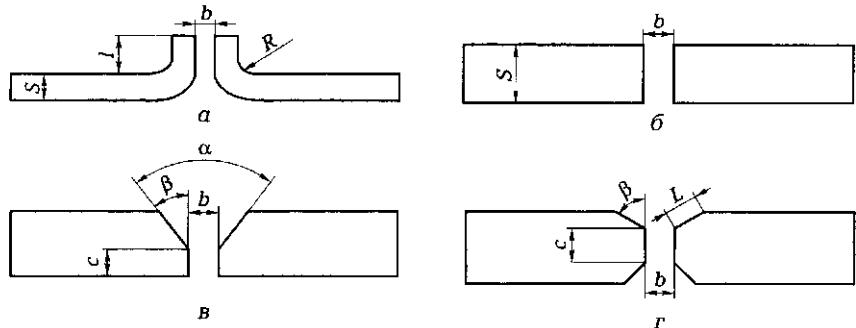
Основные формы [a—*г*] разделки кромок для сварки стыковых соединений:
